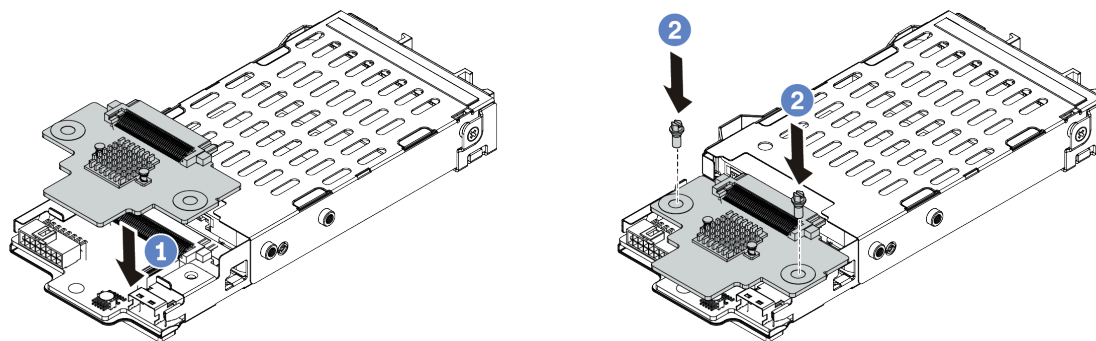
Installation d'un fond de panier d'unité 7 mm (haut)
